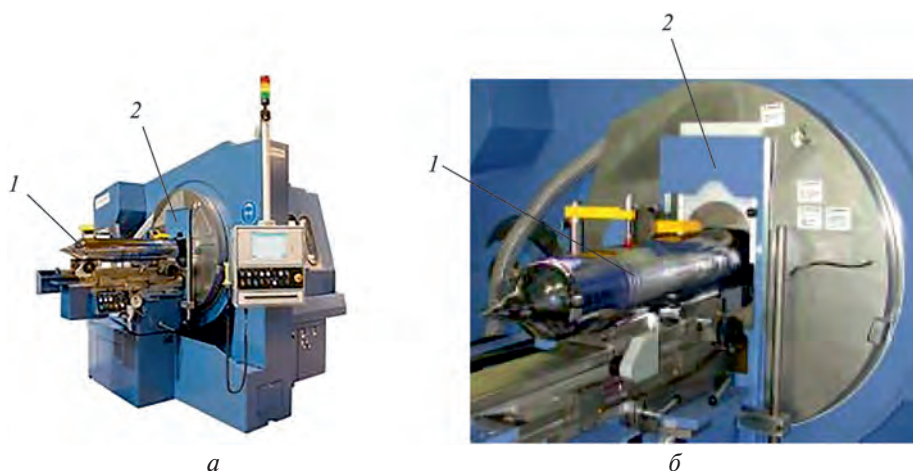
Установка для резки слитков внутренним режущим кругом:
